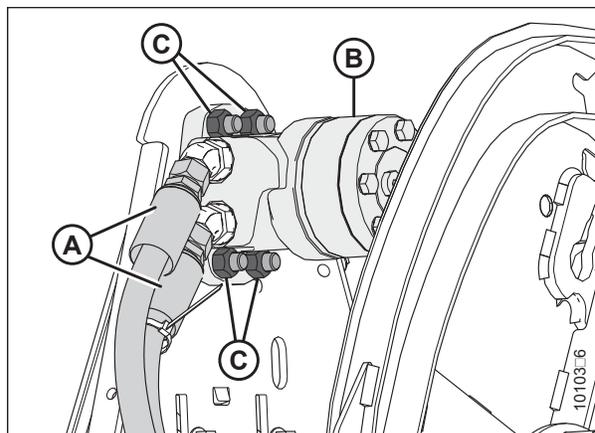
Haspelmotor und Hydraulikschläuche
